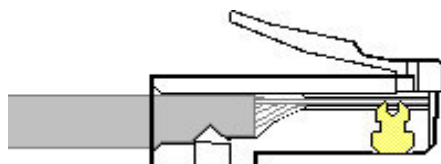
Внешний вид обжатого разъема RJ-45
